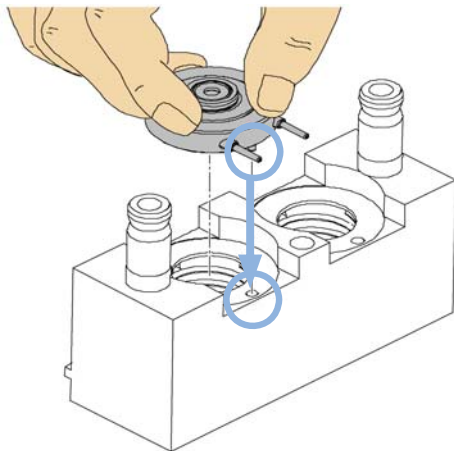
Insertion des bagues supports de l'accessoire de rinçage de joint en continu.
